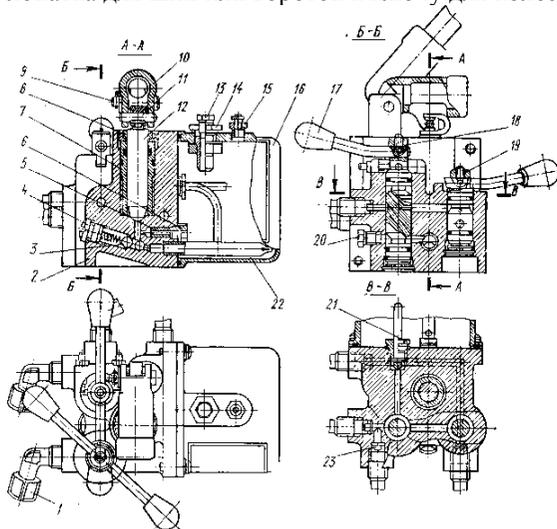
Насос опрокидывания кабины и подъема запасного колеса:
